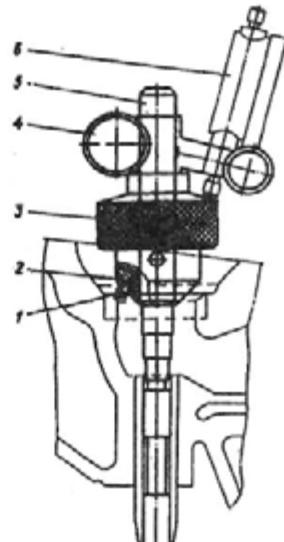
Приспособление для проверки биения фаски из седла клапана:
